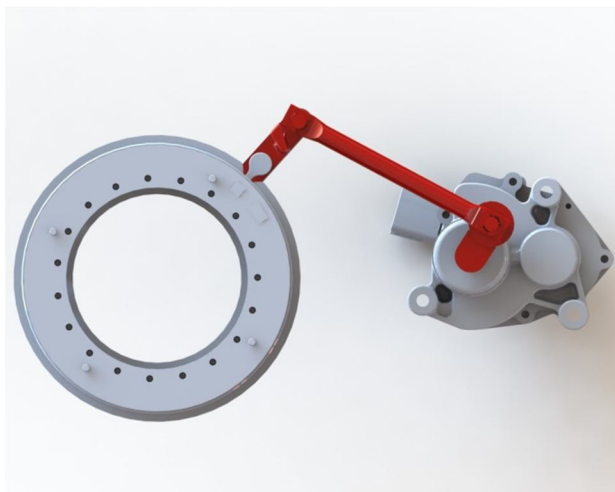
Model VNT mechanismu s elektromotorem od firmy Honeywell
